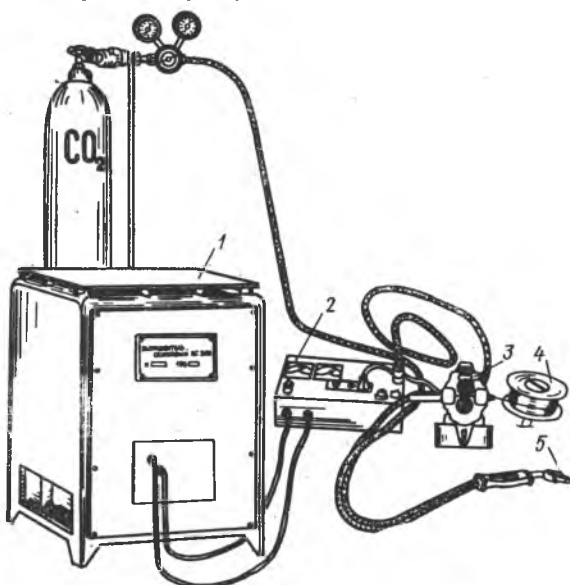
Общий вид полуавтоматической установки А-825М:
